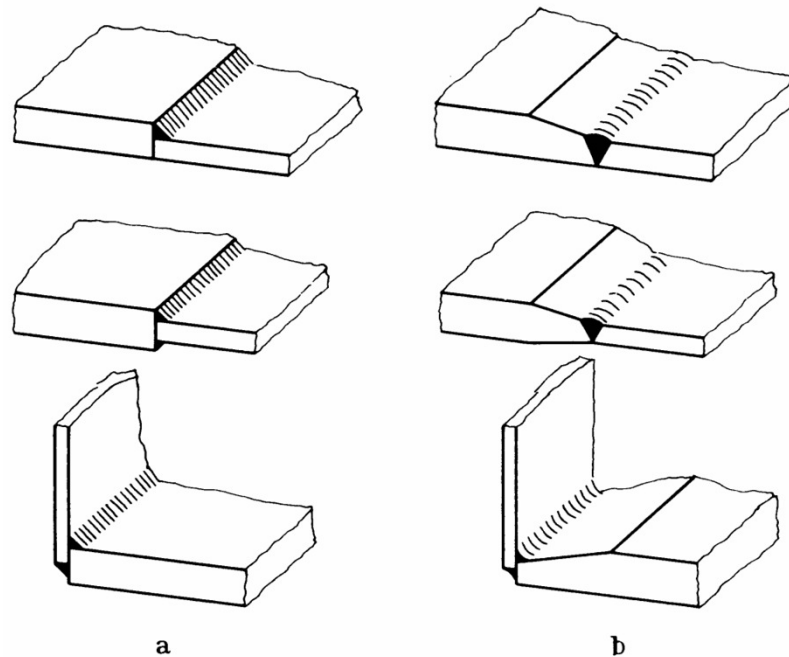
, b. Querschnittsübergänge an Schweißteilen a ungünstige Gestaltung;
